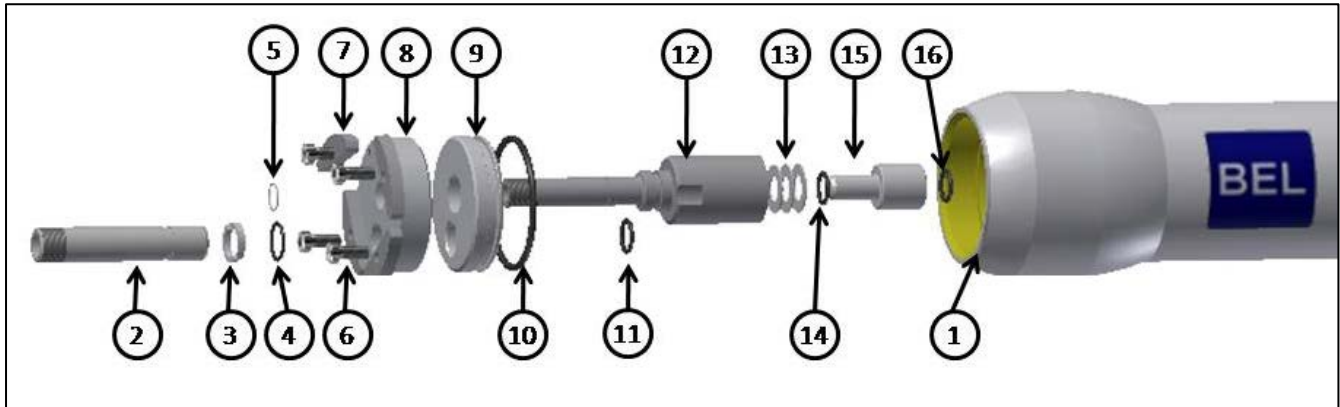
Despiece Cabeza tubo BEL 4" 600/1000/1200 psi – Endport
